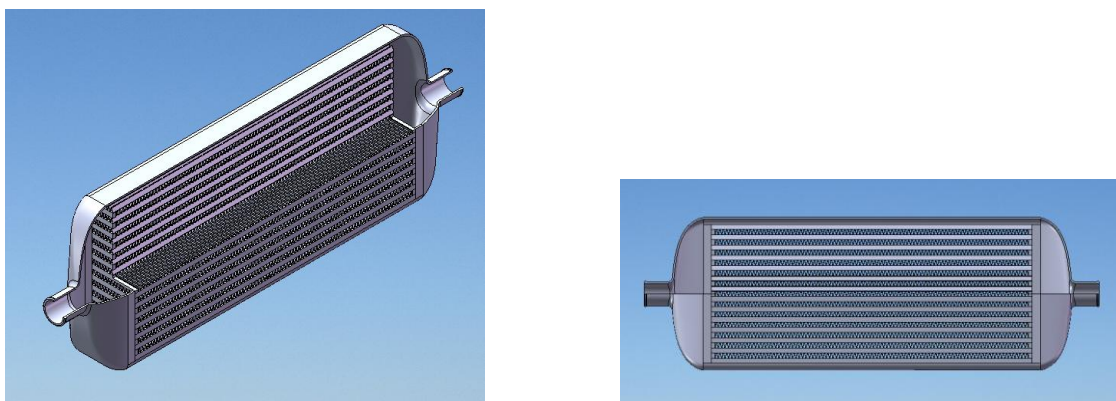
Corte ¼ del Intercooler 3D (1)
